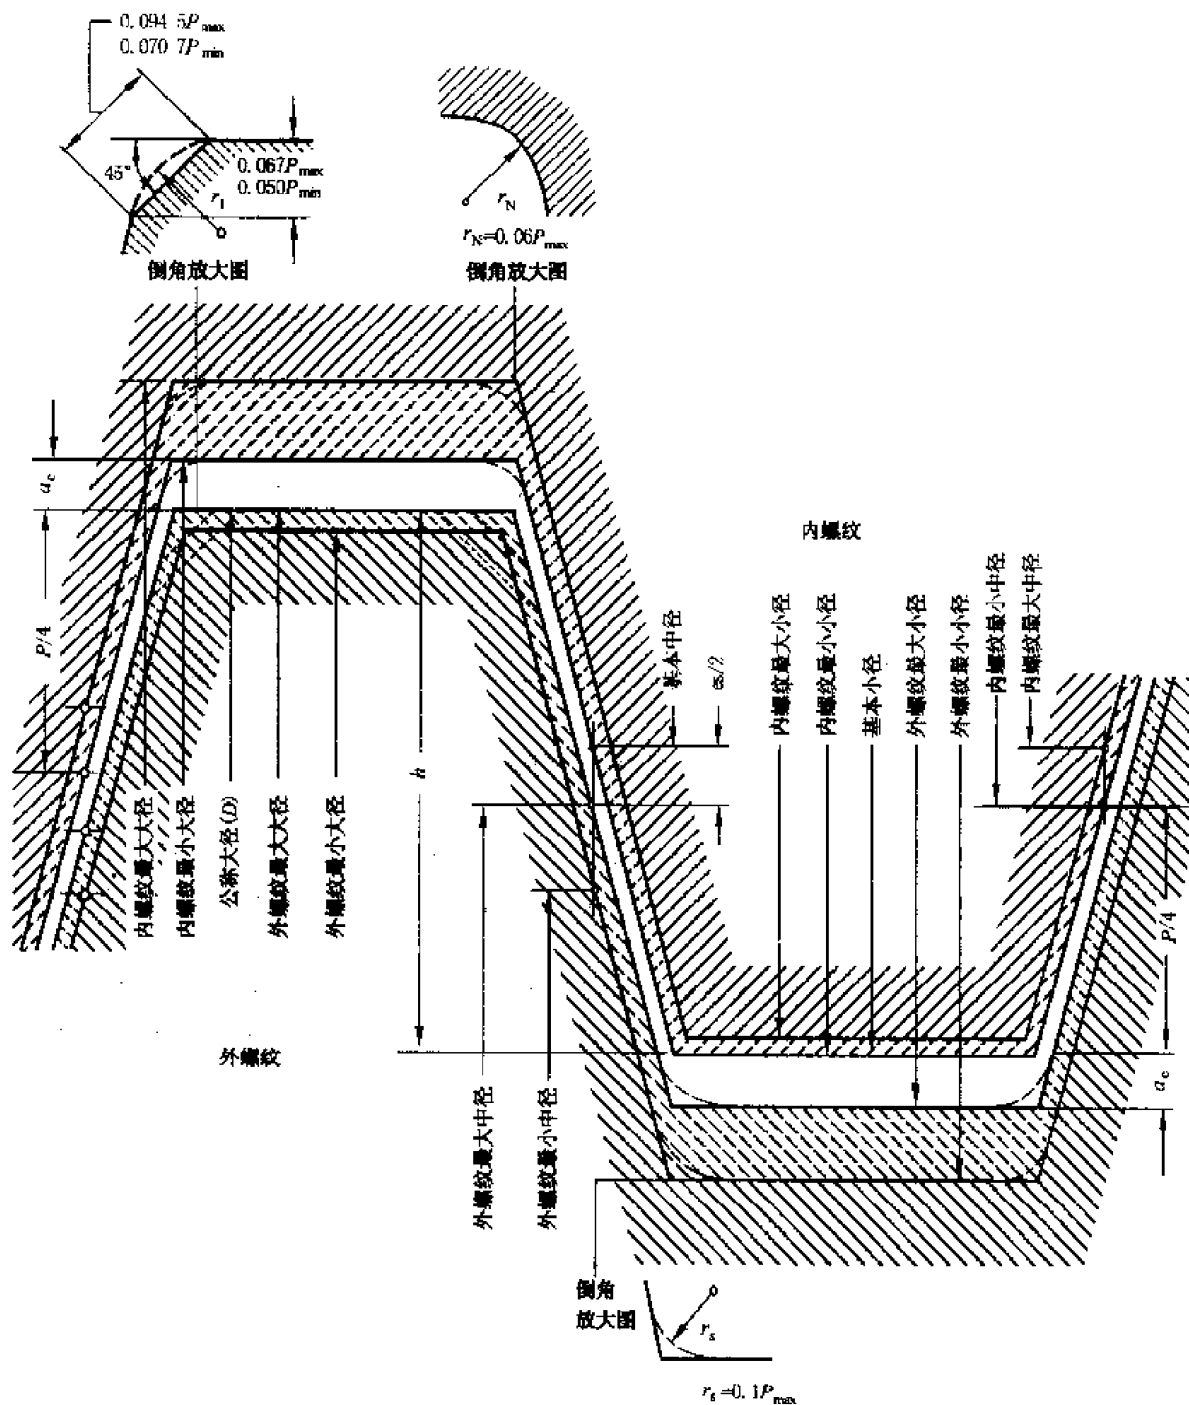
一般用途爱克母螺纹的公差带位置
